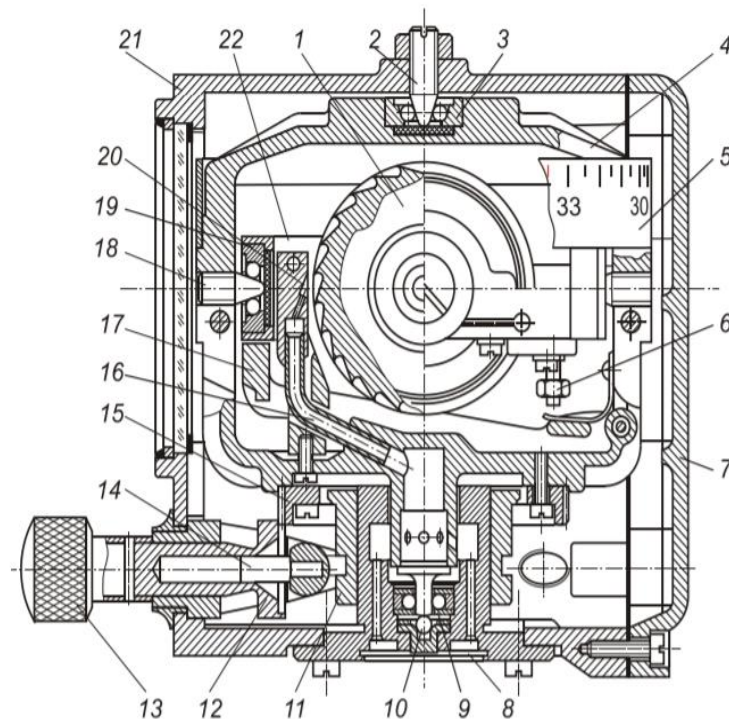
[3] 1 - ротор; 2 - центр регульований; 3 - підшипник; 4 - зовнішня рамка; 5 - шкала; 6 – гвинт балансування; 7 - кришка корпусу; 8 - фільтр; 9 - шарикопідшипник; 10 - куля; 11 - втулка аретира; 12 - торцева шестерня; 13 - ручка; 14 - штифт вилки; 15 - шестерня; 16 - трубопровід; 17 -
